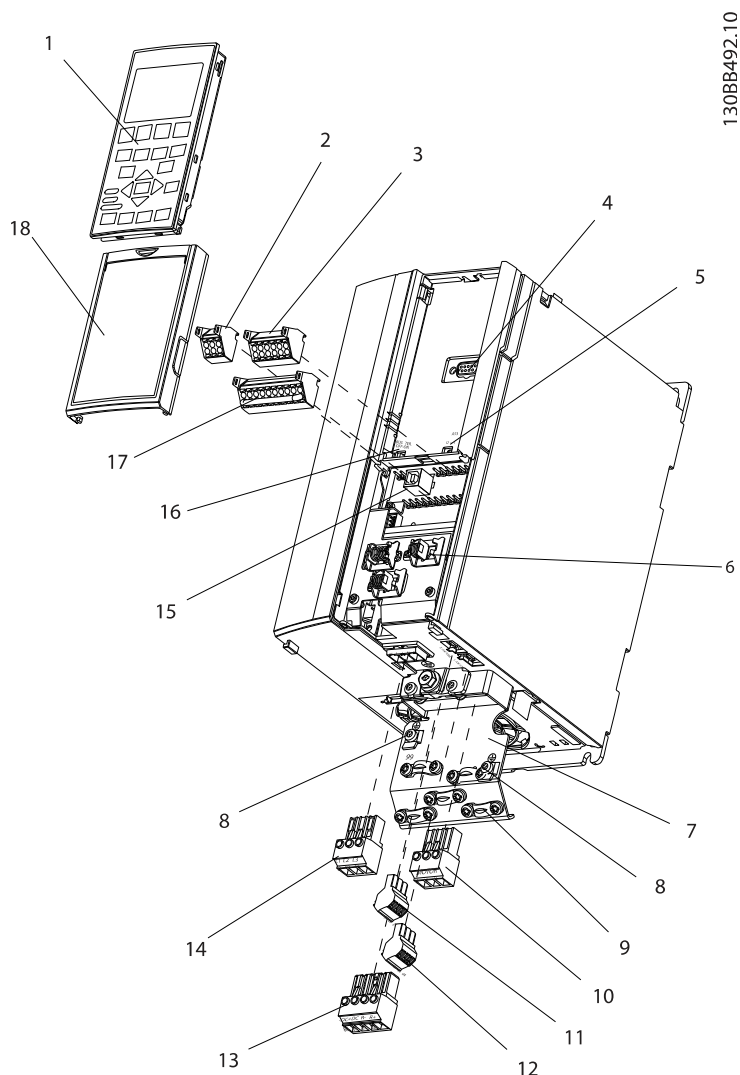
Explosionszeichnung Gerätegrößen 12-13, IP20
